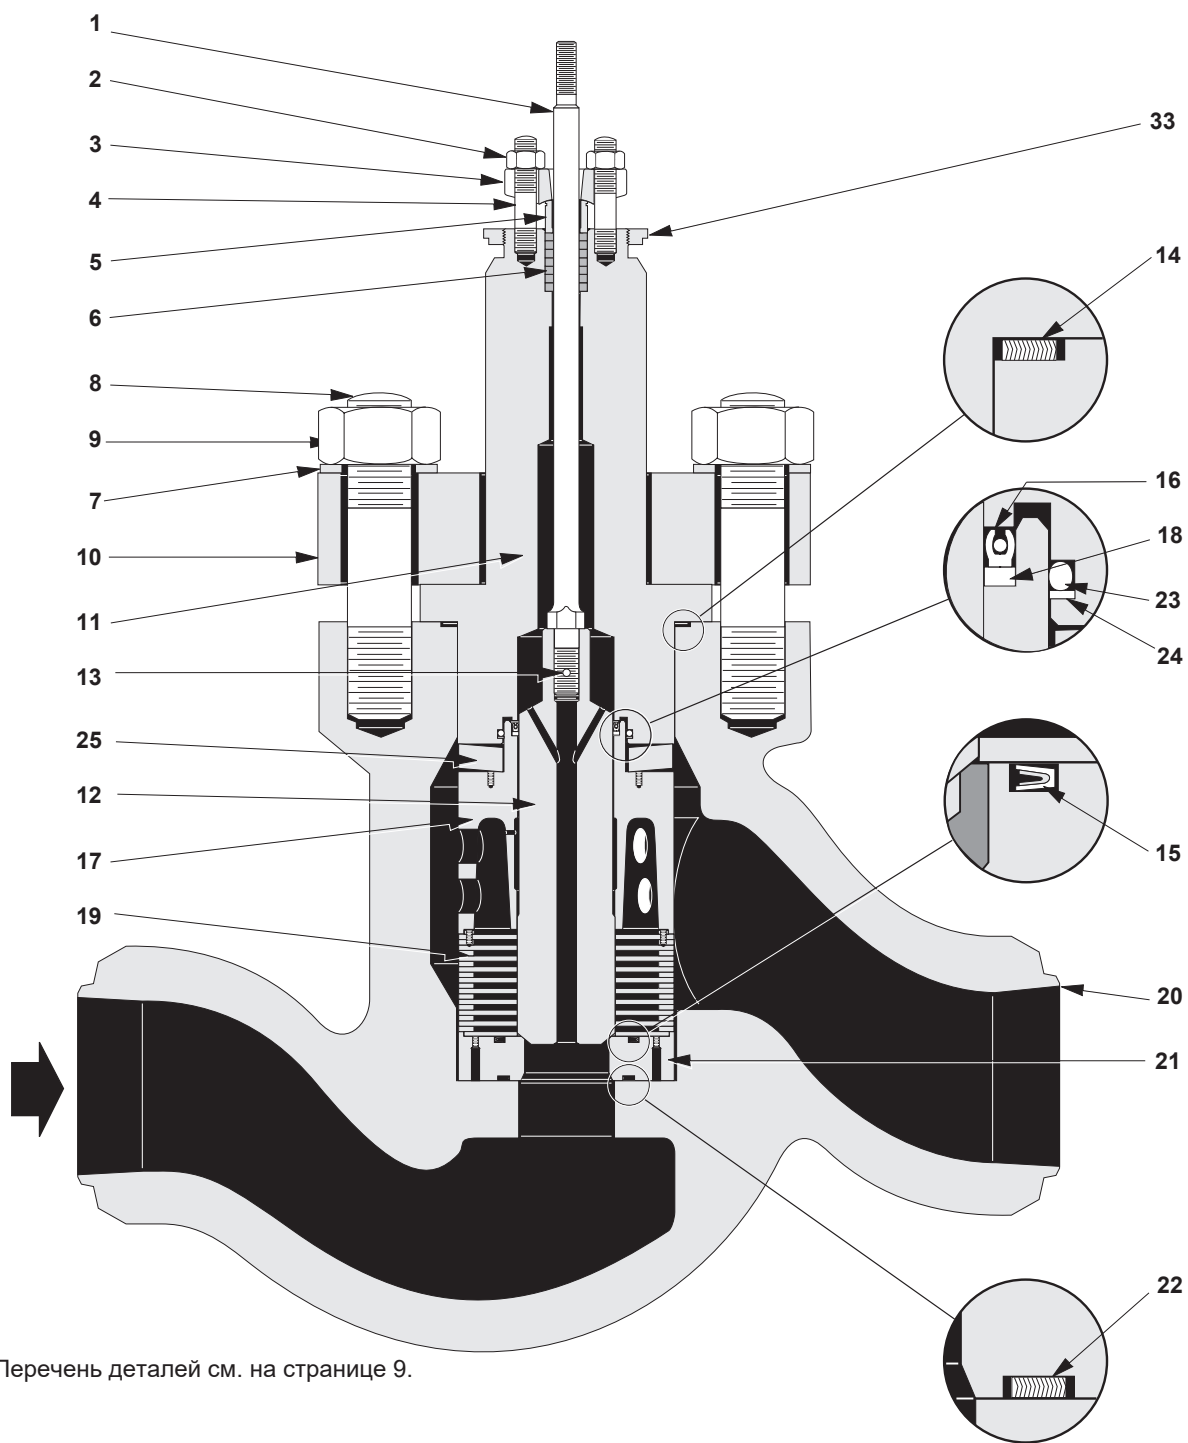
Пример конструкции литого корпуса с концами под приварку встык
